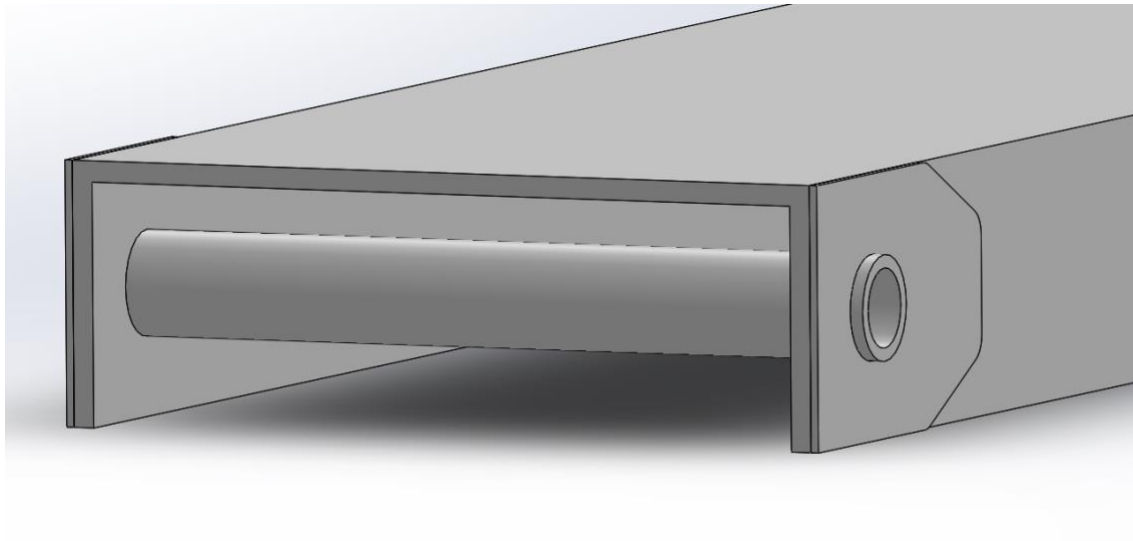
Resultado de las chapas soldadas y el casquillo dimensionado
